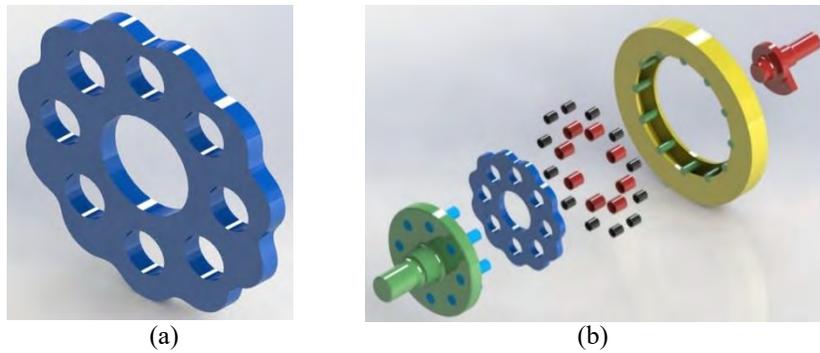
Reductor cicloidal: (a) Engrane cicloidal; (b) vista explosionada
